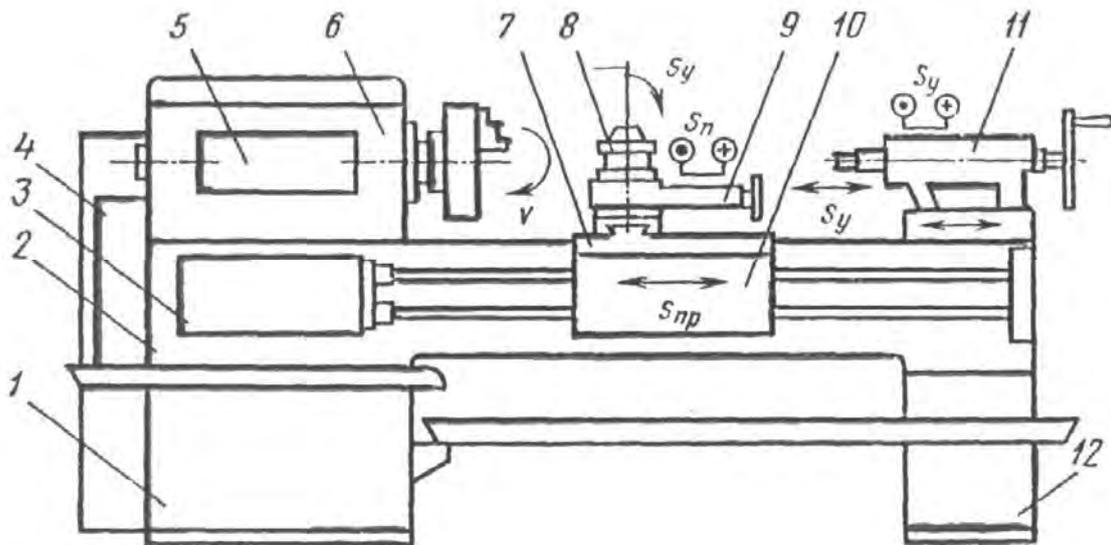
Общий вид токарно-винторезного станка 16К20
